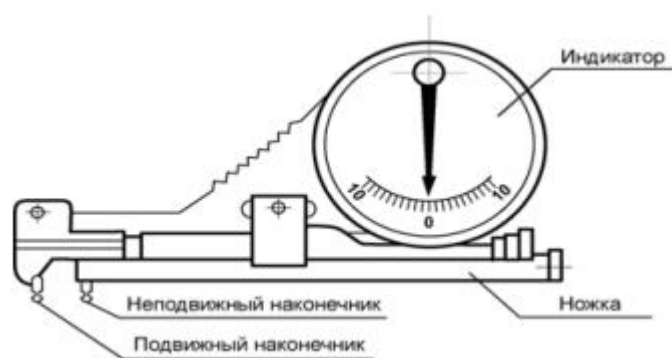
Конструкция индикаторного прибора (шагомера) с двумя наконечниками
